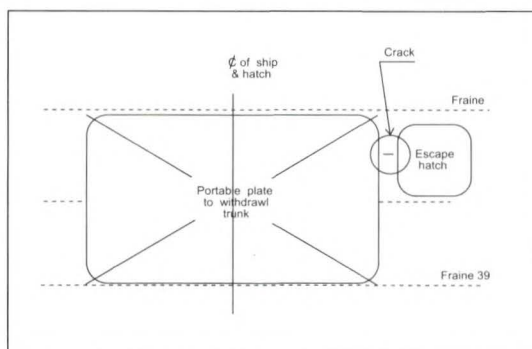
Agrietamiento en aberturas de cubierta en destructores tipo 42.
